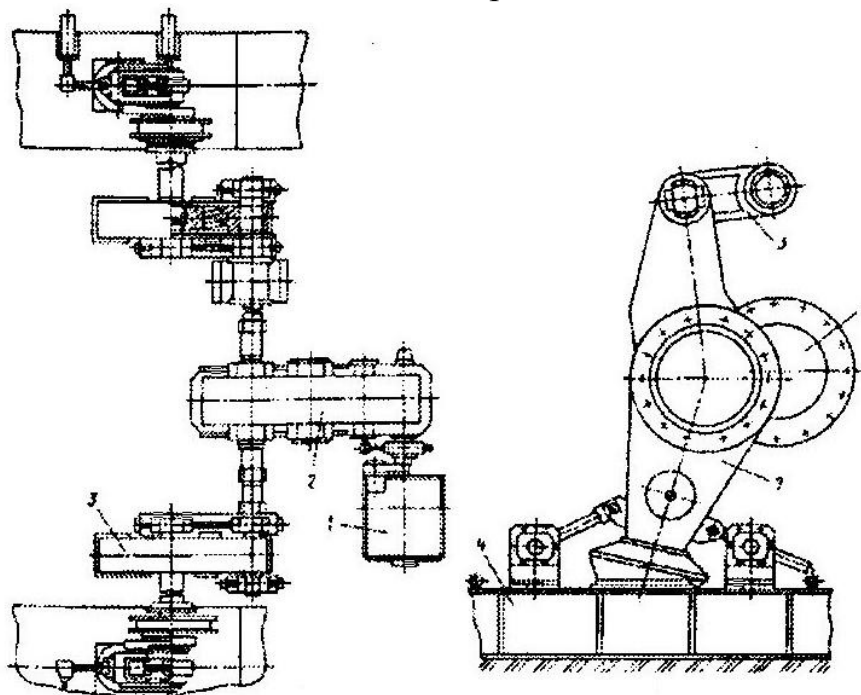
Чертеж кривошипно-рычажного механизма шагания
